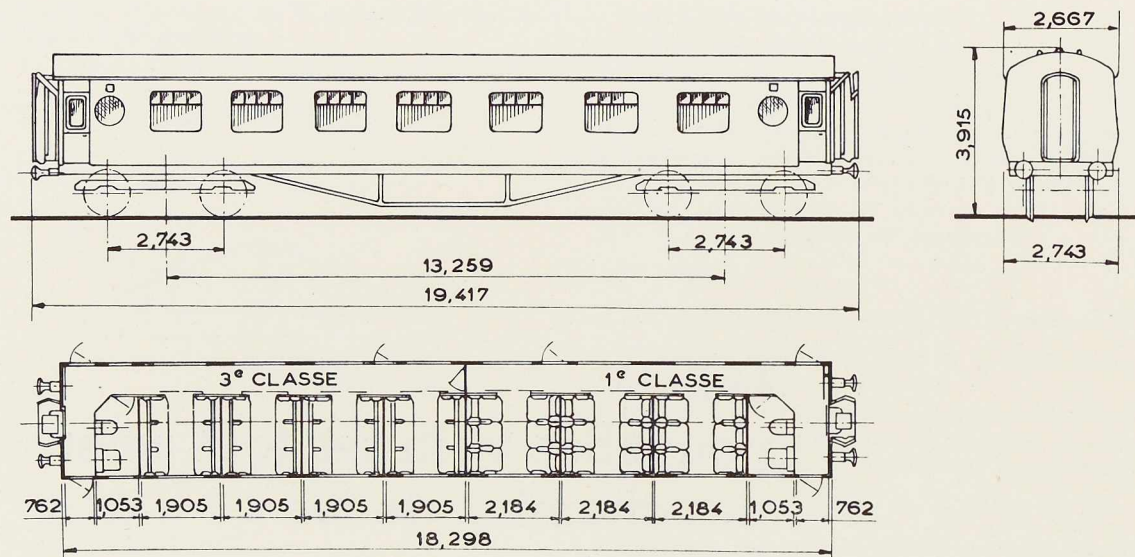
Elévation et plan d'une voiture tout acier de 1^{re} et 3^e classes.
